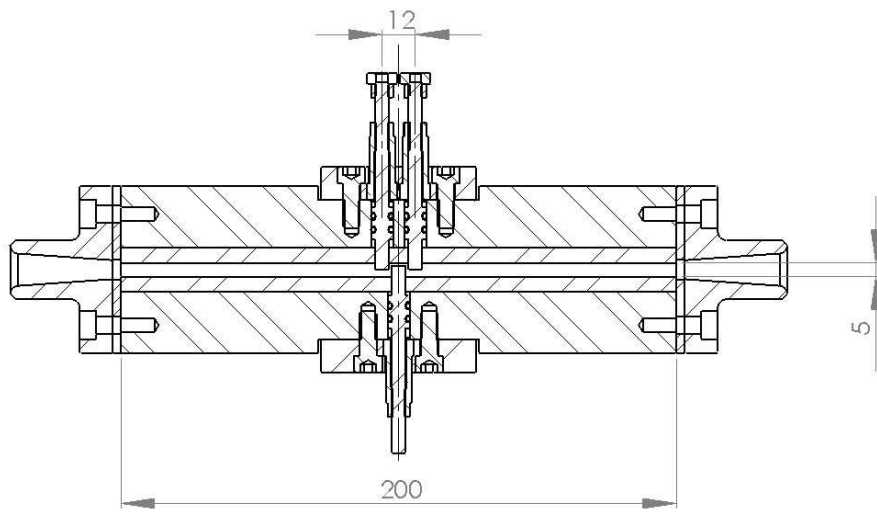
Vista em corte da seção de testes com as gavetas parcialmente fechadas
